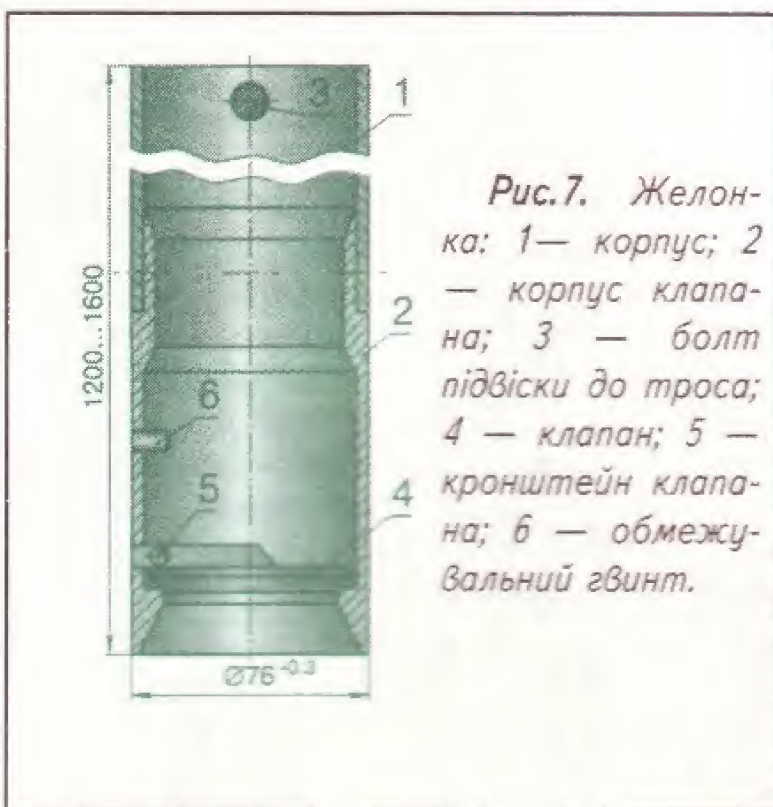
Желонка: 1 — корпус; 2 — корпус клапана; 3 — болт підвіски до троса; 4 — клапан; 5 — кронштейн клапана; 6 — обмежувальний гвинт.
